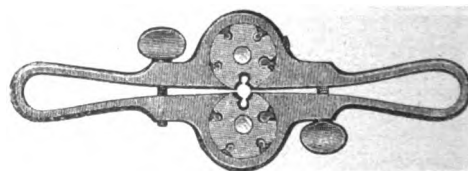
Adjustierbare Gewinde-Schneidkluppe von Winter Brothers in Wrentham.
